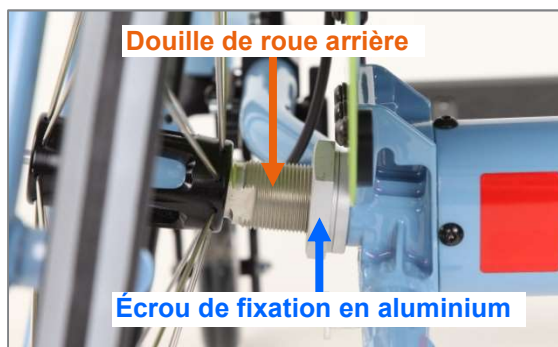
Douille de roue d'entraînement et écrou de fixation en aluminium (vue arrière)
